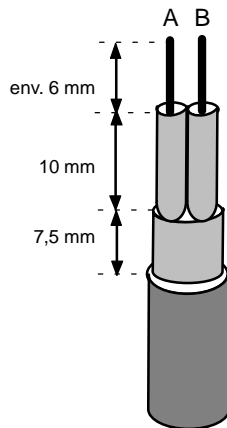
Préparation des extrémités de câble pour le montage du connecteur de bus à sortie de câble axiale
